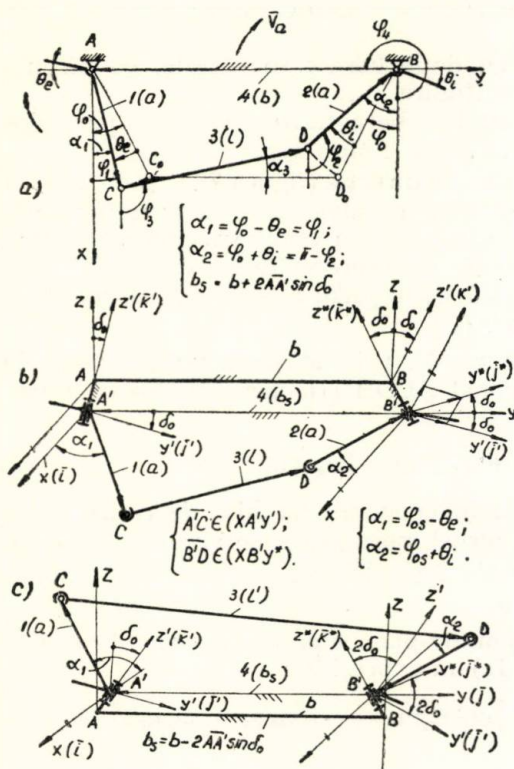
Trapez de direcție posterior, plan (a) — spațial (b), și anterior (c) — spațial
